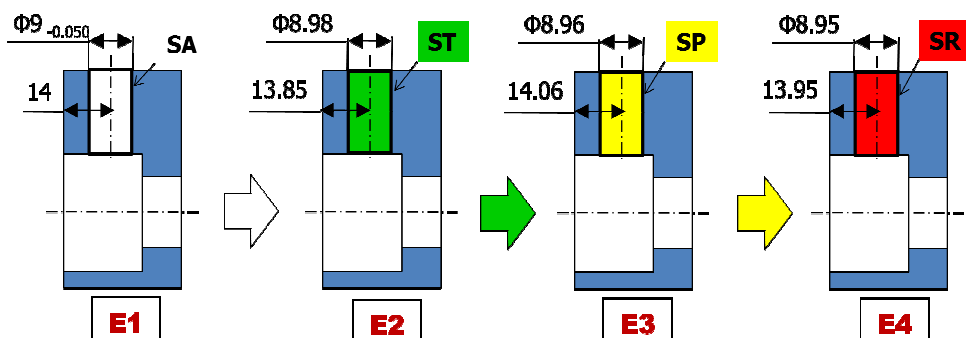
Principalele etape de realizare dimensională a unei suprafețe
